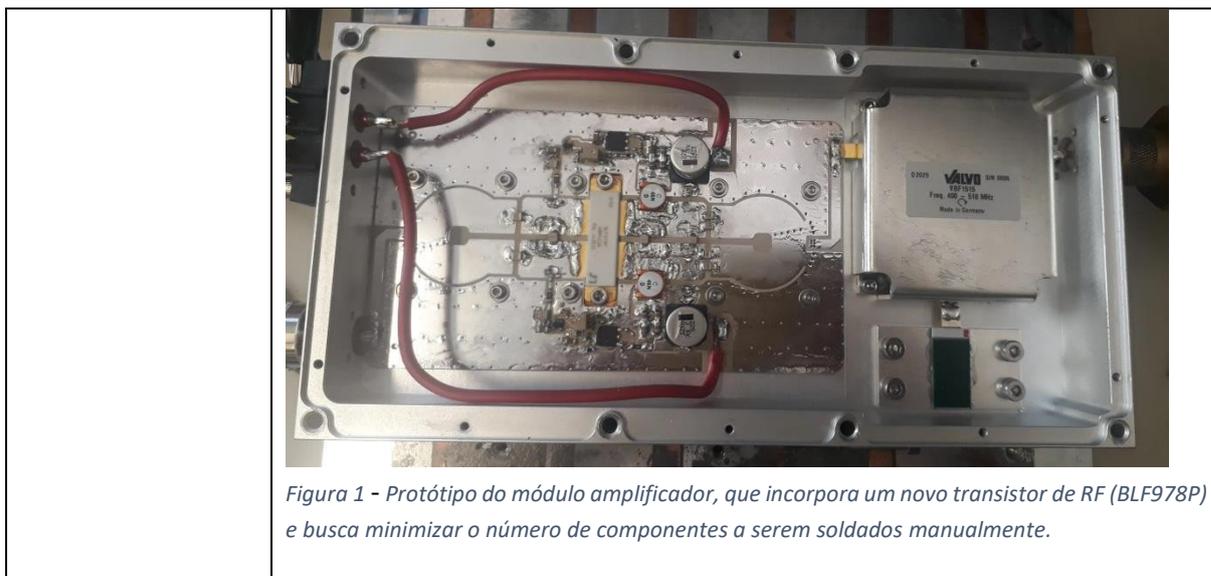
Protótipo do módulo amplificador, que incorpora um novo transistor de RF (BLF978P) e busca minimizar o número de componentes a serem soldados manualmente.
